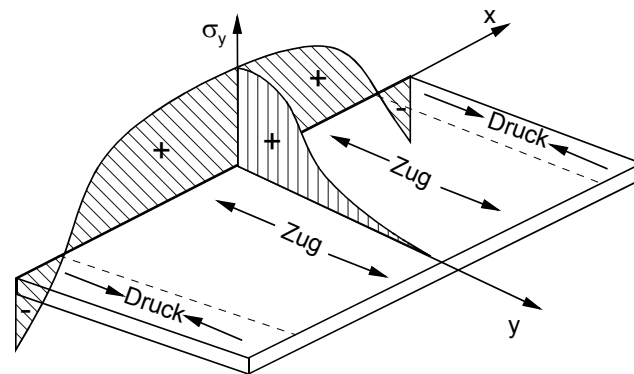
Spannungsverlauf in y-Richtung einer Rechteckplatte (symmetrisch zur Schweißnaht)
